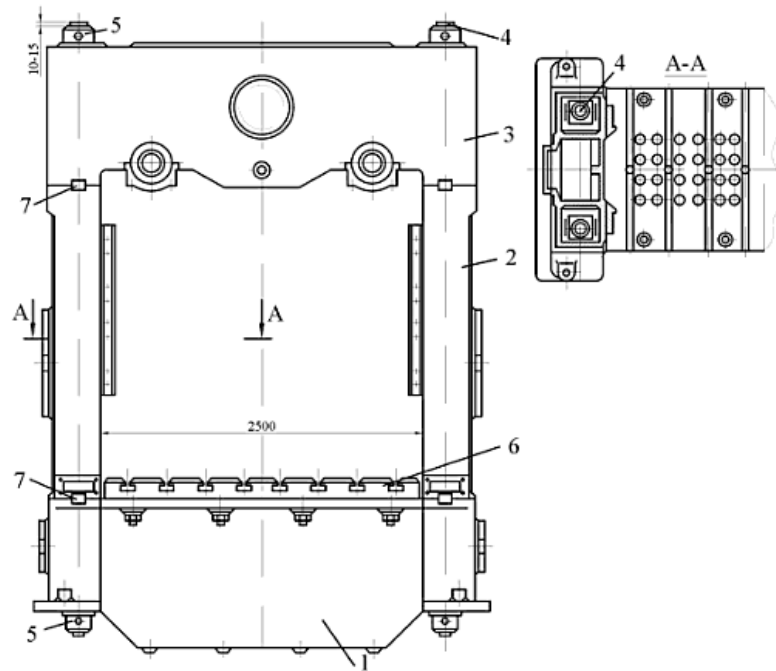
Зварна станина вертикального закритого двокривошипного листоштампувального преса: 1 – нижня траверса зі столом; 2 – стойка; 3 – верхня траверса; 4 – стяжні стержні; 5 – гайки стяжних стержнів; 6 – підштамова плита; 7 – шпонки стійок
